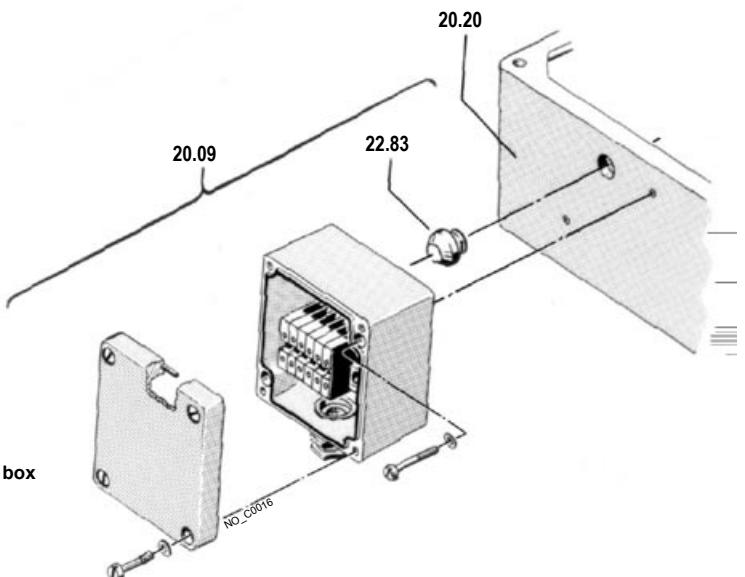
d: Anbau eines Klemmenkastens 1XB3 020
